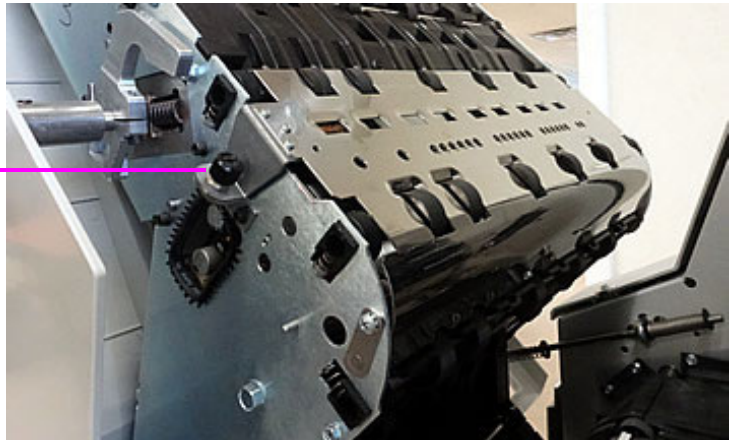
Rändelschraube des Grafikdruckers lockern
